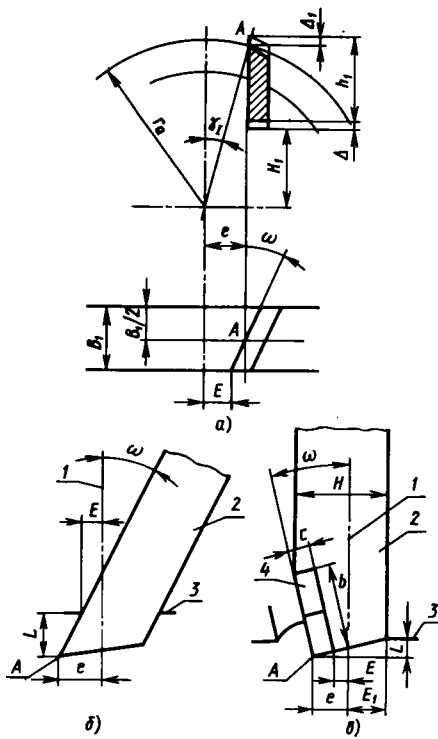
Схема к расчету параметров паза под нож в корпусе фрезы
